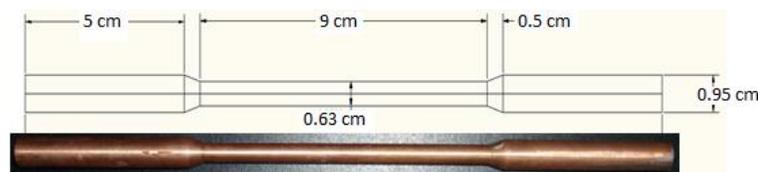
Probeta de cobre maquinada para las pruebas de ensayos de tensión-corrosión.
